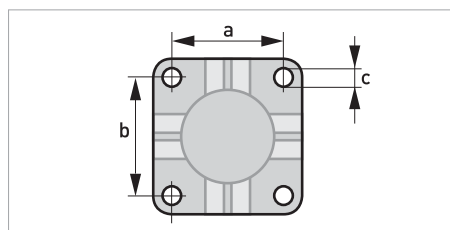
Dimensiones para placa de montaje del alojamiento de campo
